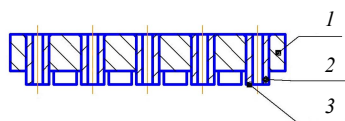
Конструкция питателя, оснащенного жаростойкими вставками: 1 – корпус; 2 – керамическая вставка; 3 – покрытие
